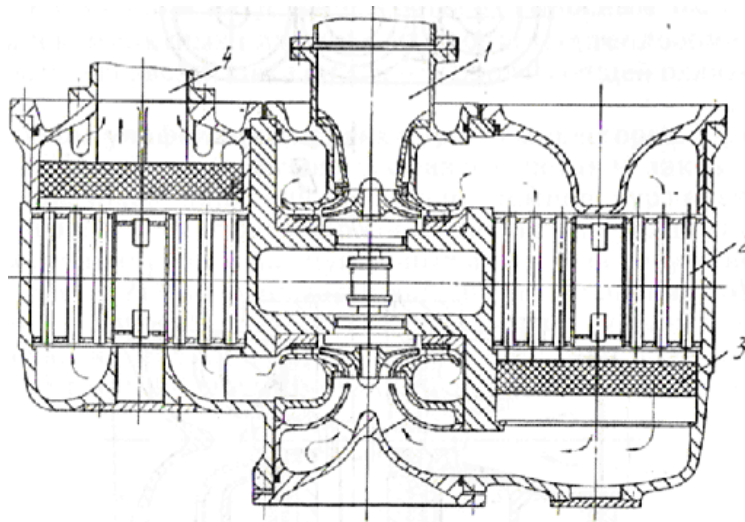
Двухвальный четырехступенчатый центробежный компрессор общего назначения (НИИТК). Разрез по одному из валов.
